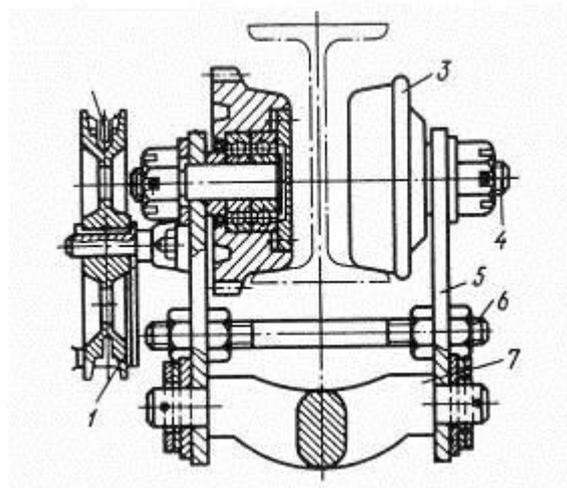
Монорельсовая тележка с ручным механизмом передвижения: 1 — приводное колесо; 2 — цепь; 3 — колеса; 4 — оси; 5 — боковые накладки; 6 — шпильки; 7 — траверса
